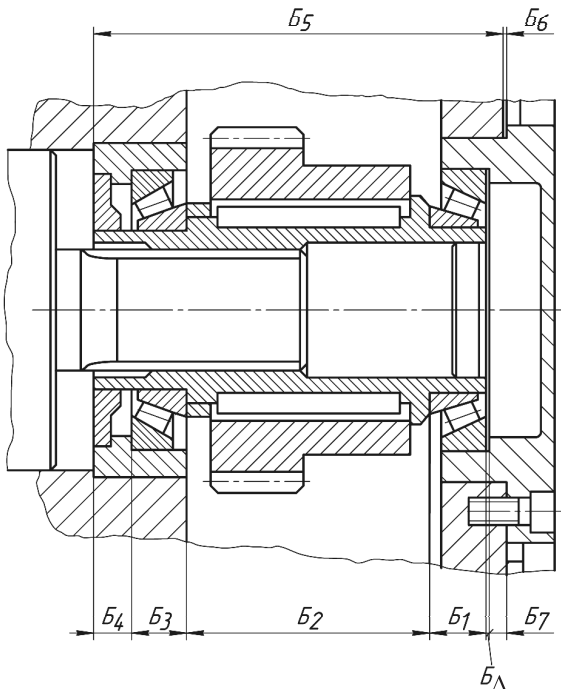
Схема задней опоры шпинделя агрегатного станка
